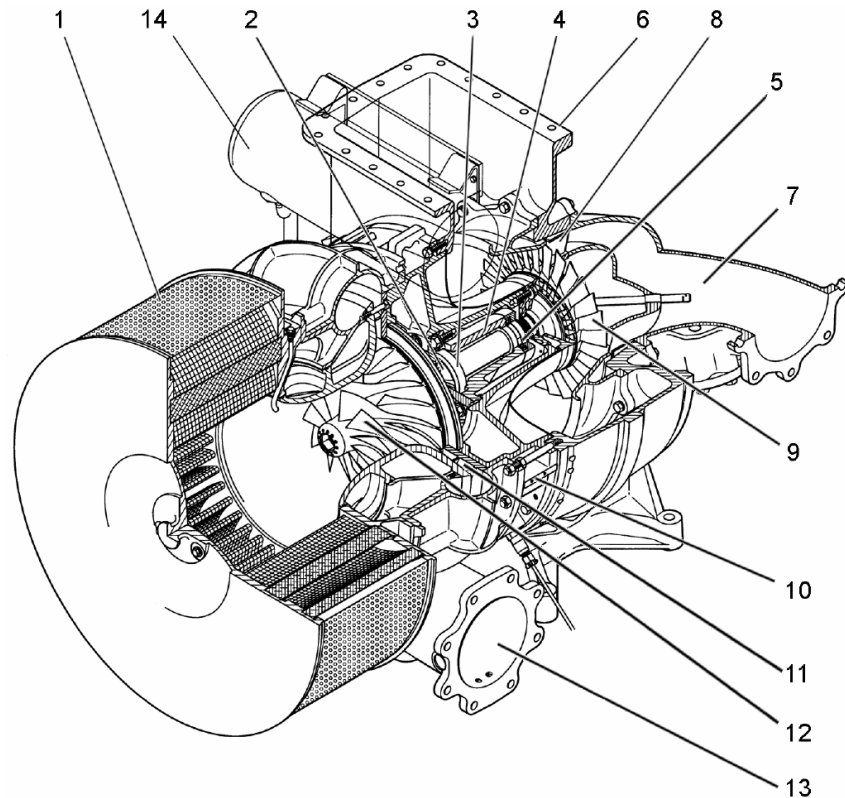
Турбокомпресор TPL80-B12: 1 – фільтр-глушник; 2,5 – підшипник ковзання; 3 – упорний підшипник; 4 – втулка підшипника; 6 – газовий випускний патрубок; 7 – газовий впускний патрубок; 8 – соплове кільце; 9 – турбінне колесо; 10 – корпус підшипника; 11 – повітряний дифузор; 12 – компресорне колесо; 13 – корпус компресора; 14 – аварійний бак масла
